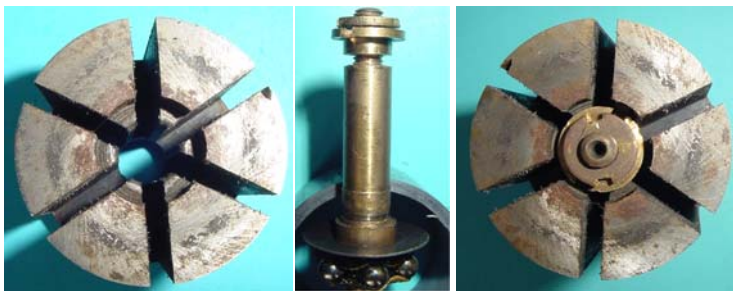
Befestigung des Magnetsystems auf der Welle
